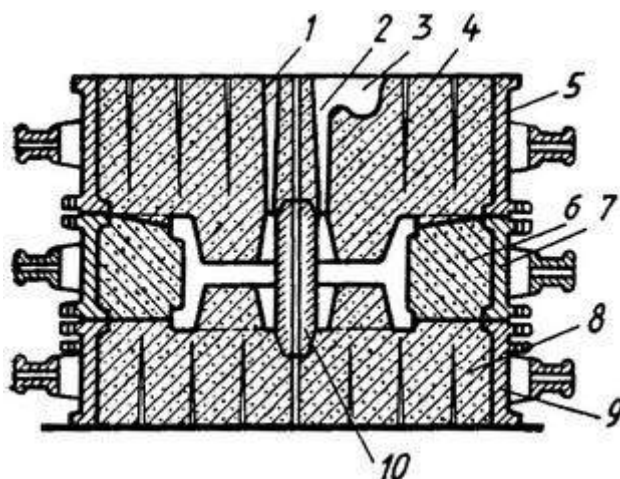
Форма для отливки шкива, изготовленная в трех опоках:
